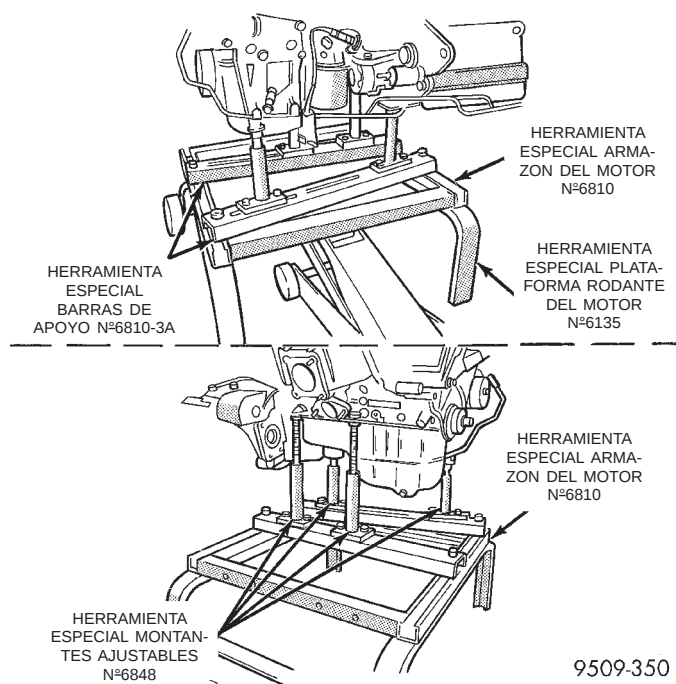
Emplazamiento de los soportes de montantes de instalación del armazón del motor
